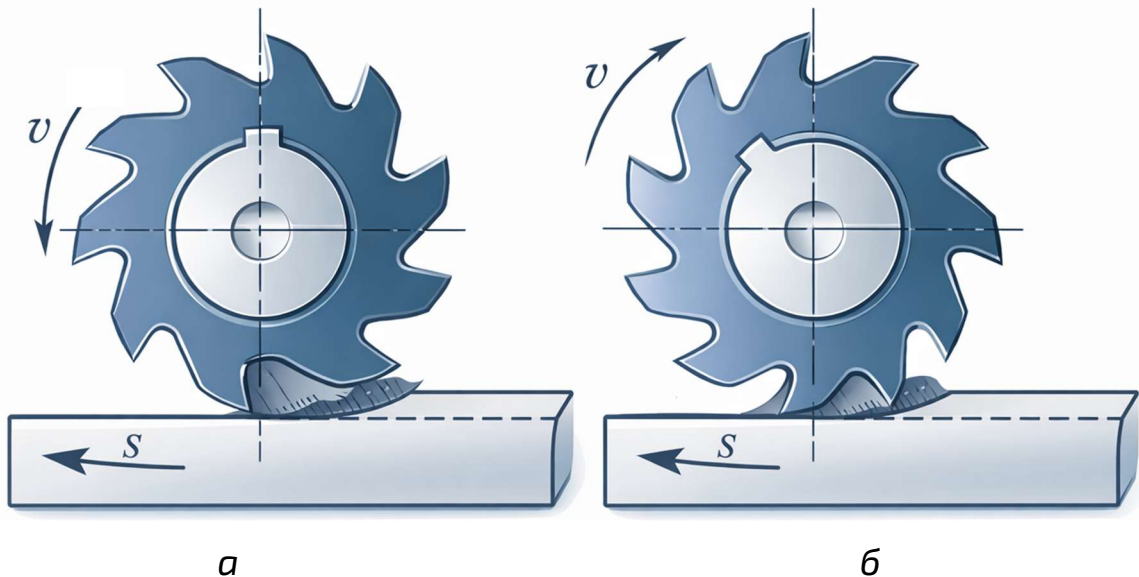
Види фрезерування: а – зустрічне, б – попутне
